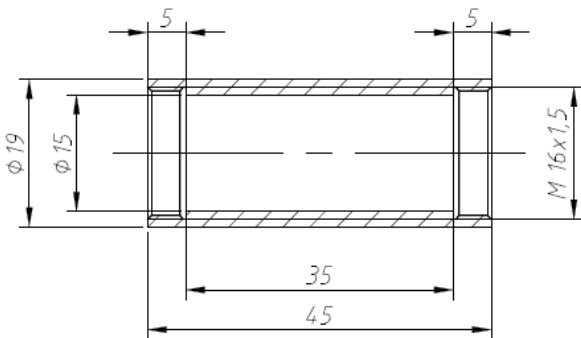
Эскиз цилиндра с засыпкой из шариков.
